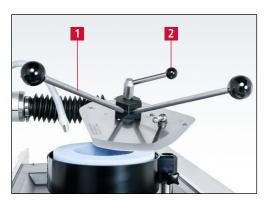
Schleifhebel auf Aufnahmebolzen montieren
